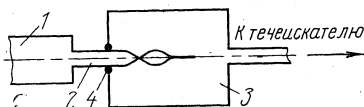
Схема проверки герметичности штуцера тепловой трубы.
